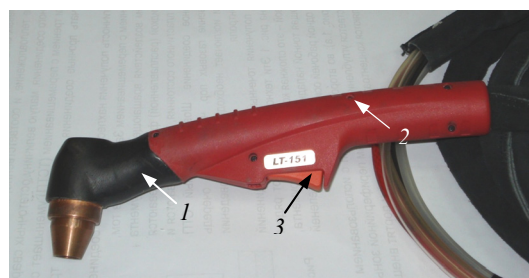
Плазменная горелка для сварки цветных металлов: 1 – плазматрон; 2 – ручка; 3 – кнопка «Пуск»
